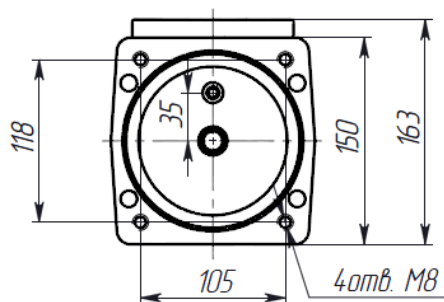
Общий вид проходного изолятора ИПУ-10-150
